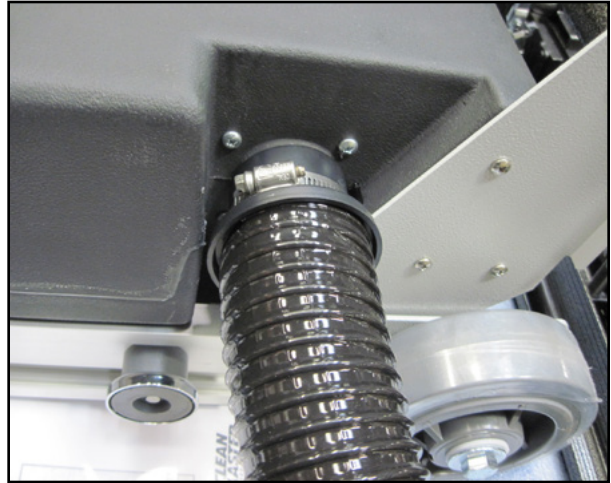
Fixer l'autre extrémité du boyau à l'assemblage du boîtier
